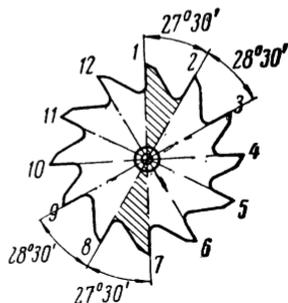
Схема расположения зубьев у развертки с неравномерным шагом
